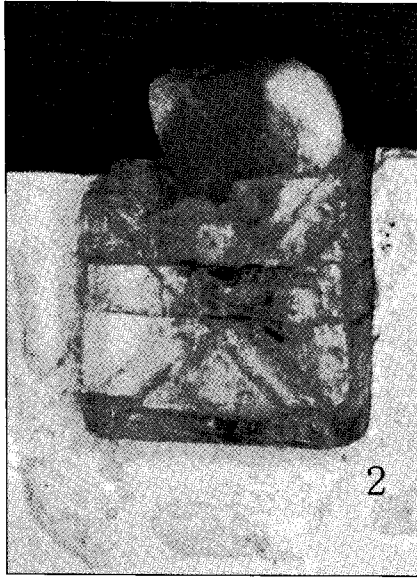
황절단 후 mold 내에 각 시편을 재 위치시킨 후의 사진
